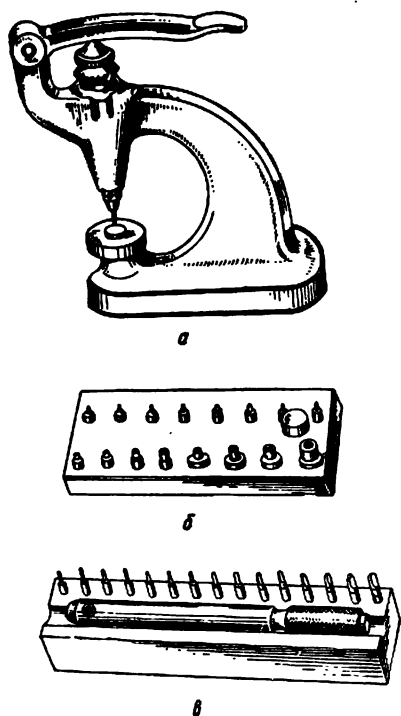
Ручной пресс для запрессовки камней: а — пресс; б — пуансоны для запрессовки; в — калибровочные развертки
